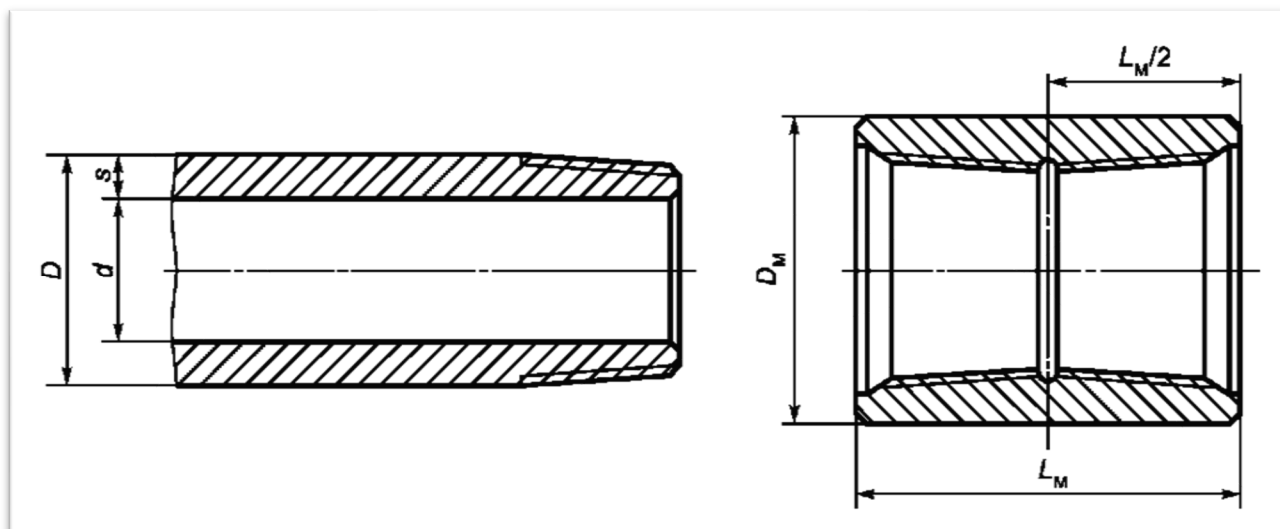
Труба и муфта с резьбовым соединением НКНН
